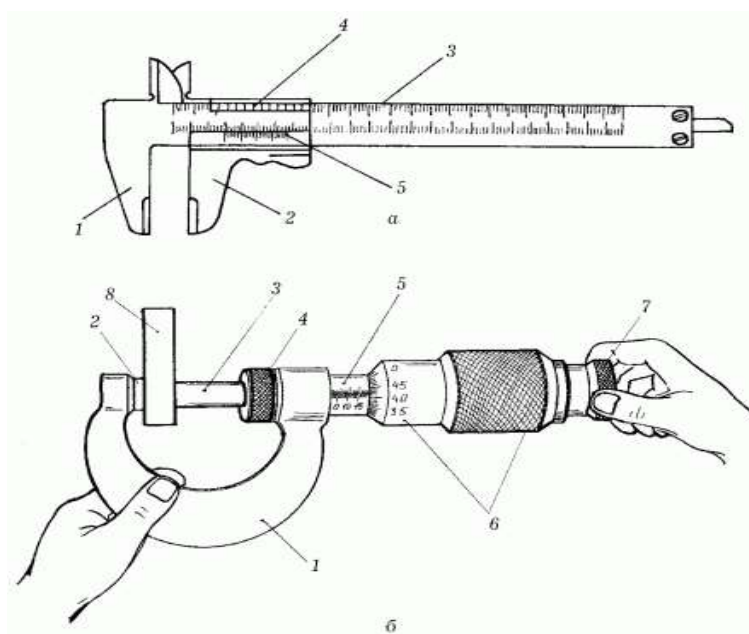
Измерительные инструменты: а – штангенциркуль: 1 – измерительные губки; 2 – рамка с измерительными губками; 3 – штанга; 4 – нониус; 5 – стопорный винт;
